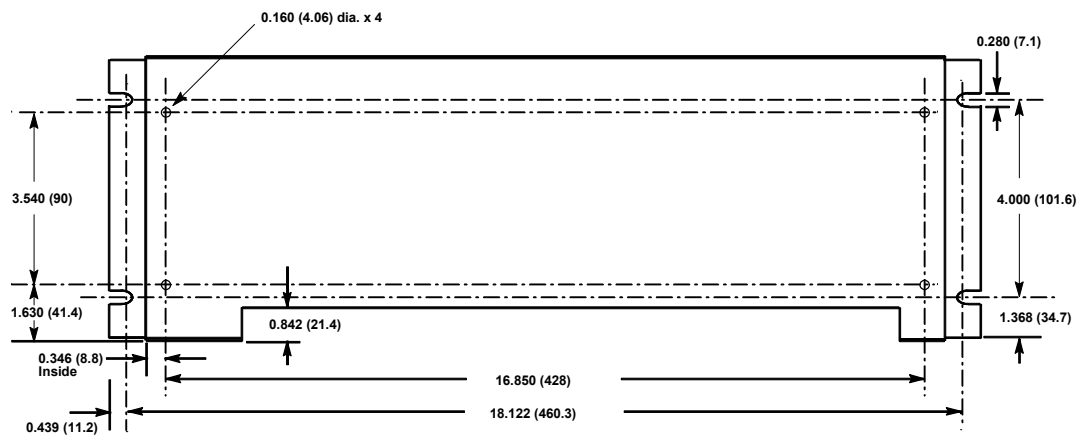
Instalace adaptéru s přední montáží IC693ACC308
